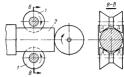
Схема опоры с непрерывным принудительным движением в направлении оси цапфы
